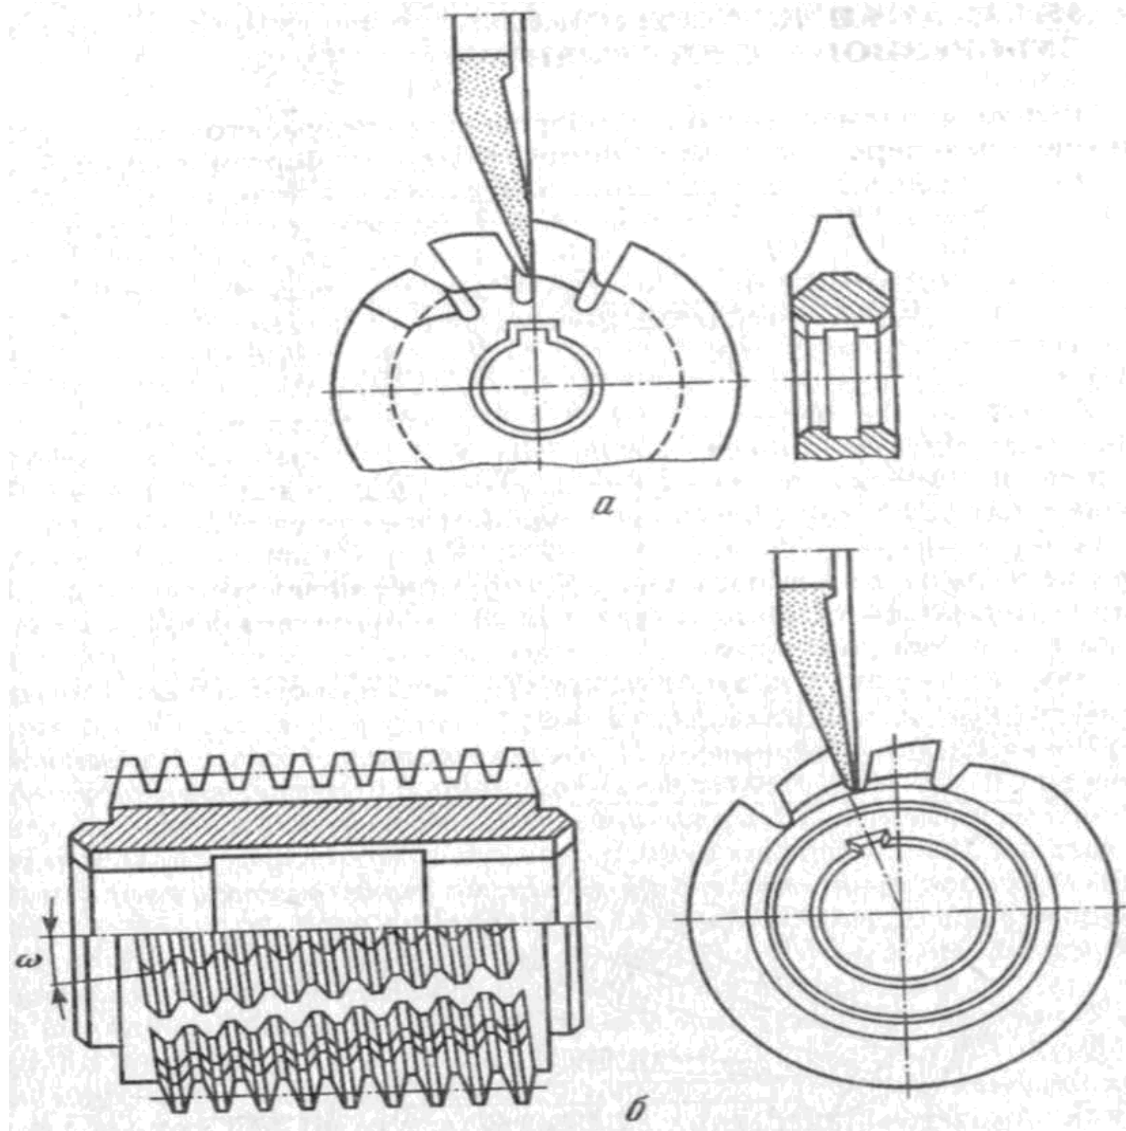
Схемы заточки зуборезных фрез: а – дисковых, б - червячных с винтовыми стружечными канавками.
